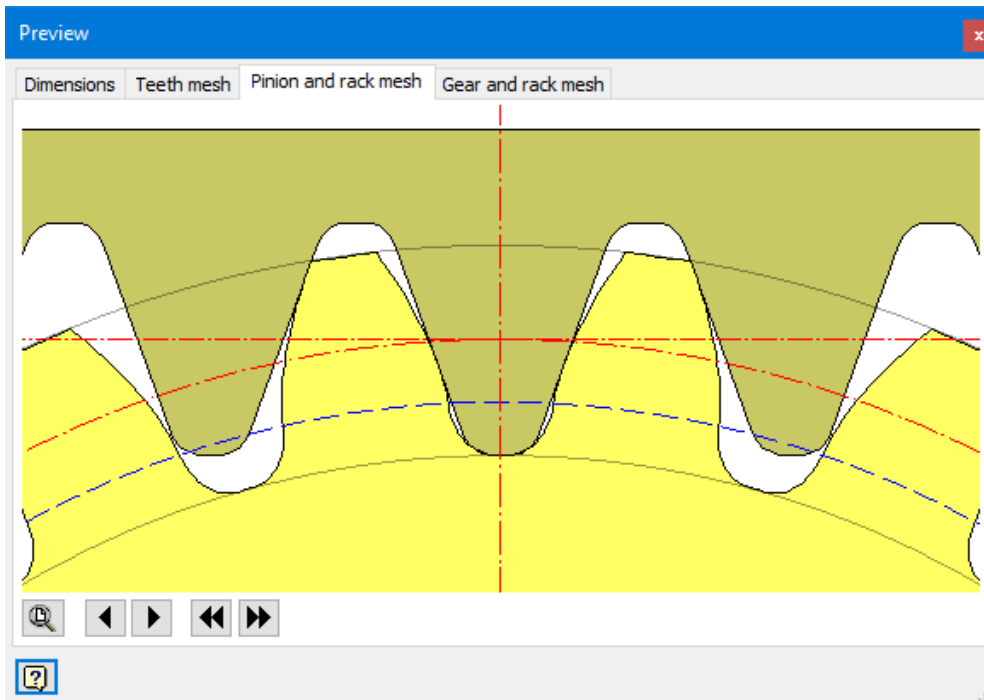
Двовимірний кресленник зачеплення шестерні і верстатної рейки
